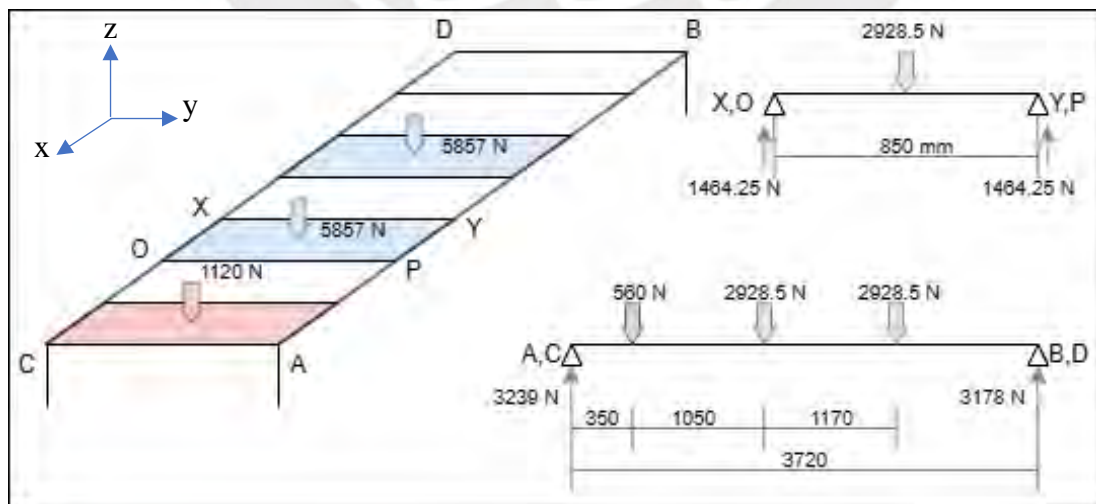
Fuerzas aplicadas sobre la estructura base y DCL de las vigas AB y XY
